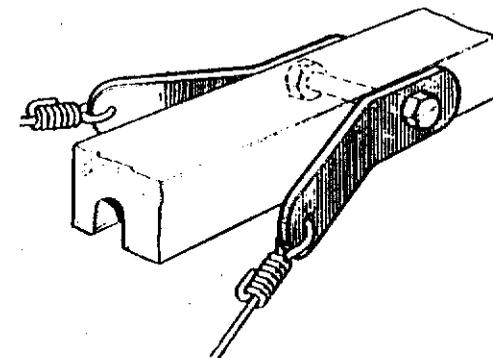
Fixation des cordes à piano sur la poutre fuselage.
